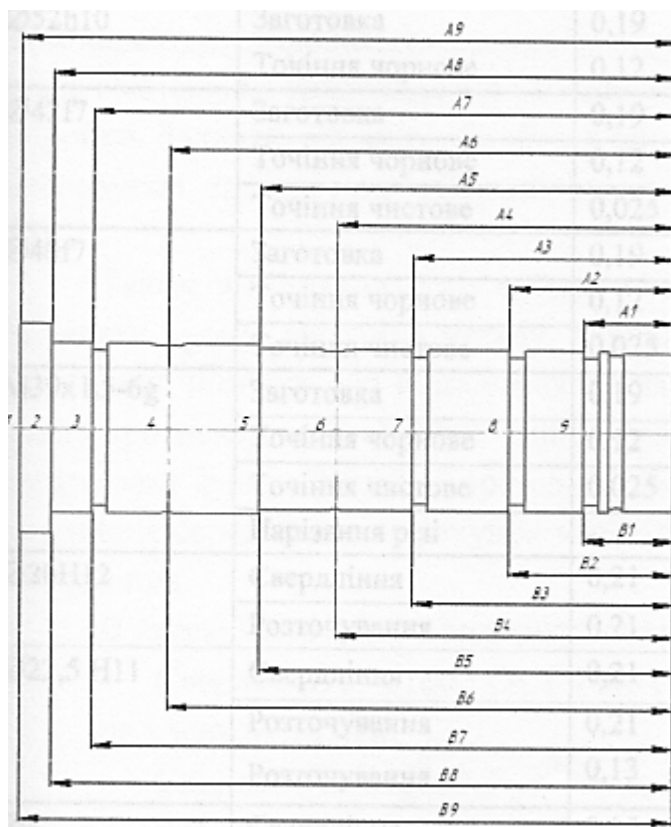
Деталь з конструкторськими та технологічними розмірами
